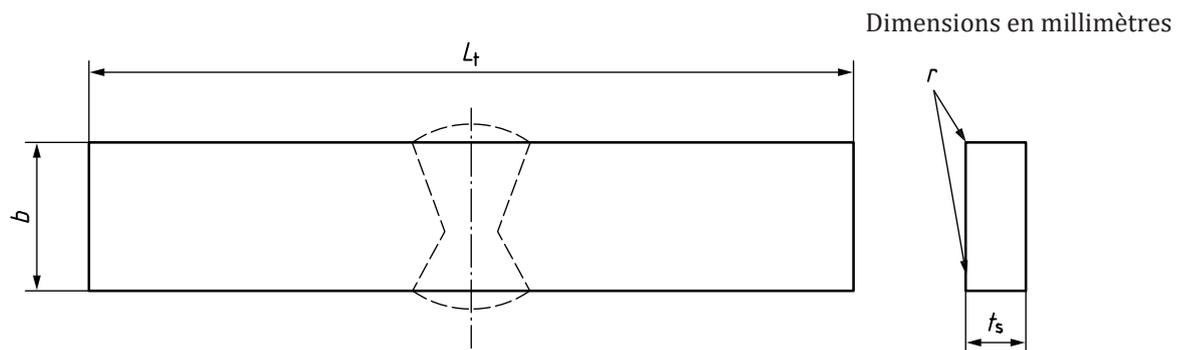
Éprouvette de pliage transversal envers sur soudure bout à bout (TRBB)
